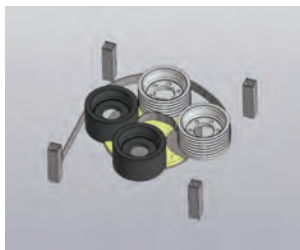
Рабочая часть стола с деталями и заготовками в позициях
